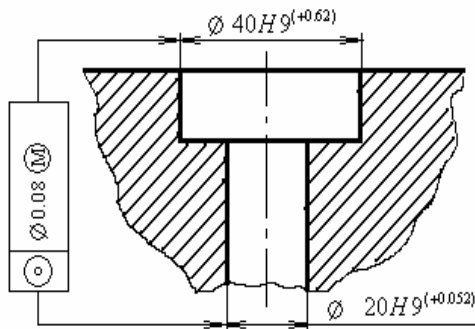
Координуючі поверхні корпусної деталі поверхні
